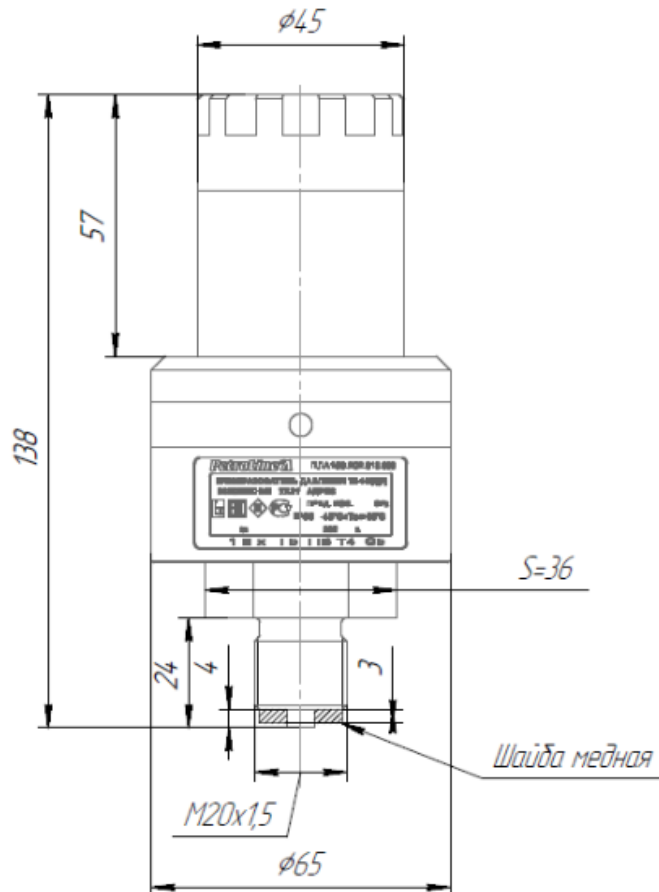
Габаритные и присоединительные размеры ТП-140Д(Р)
